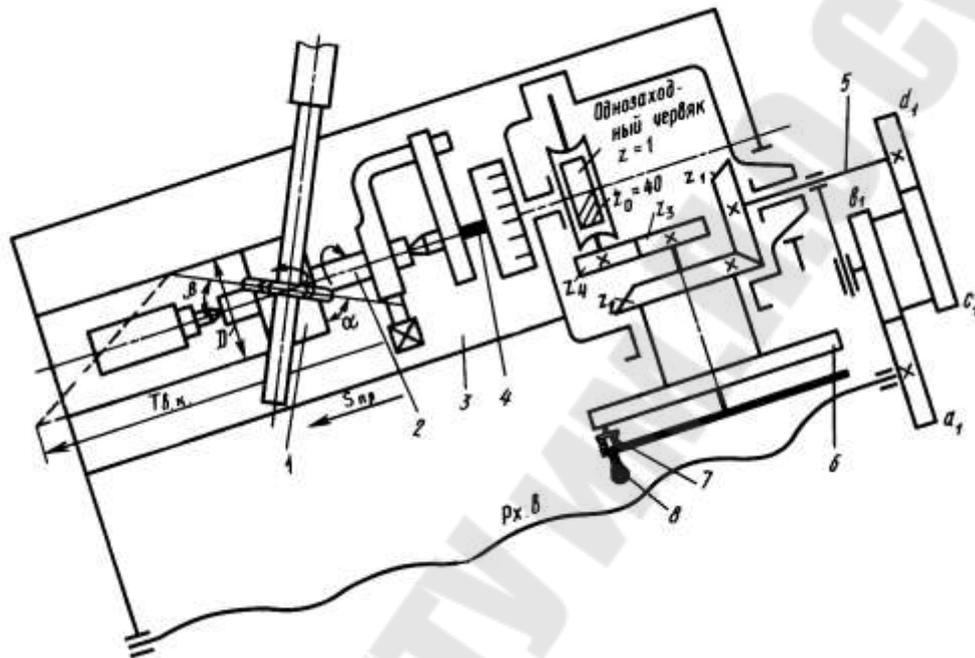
Схема наладки универсально-фрезерного станка и делительной головки на фрезерование винтовых канавок
